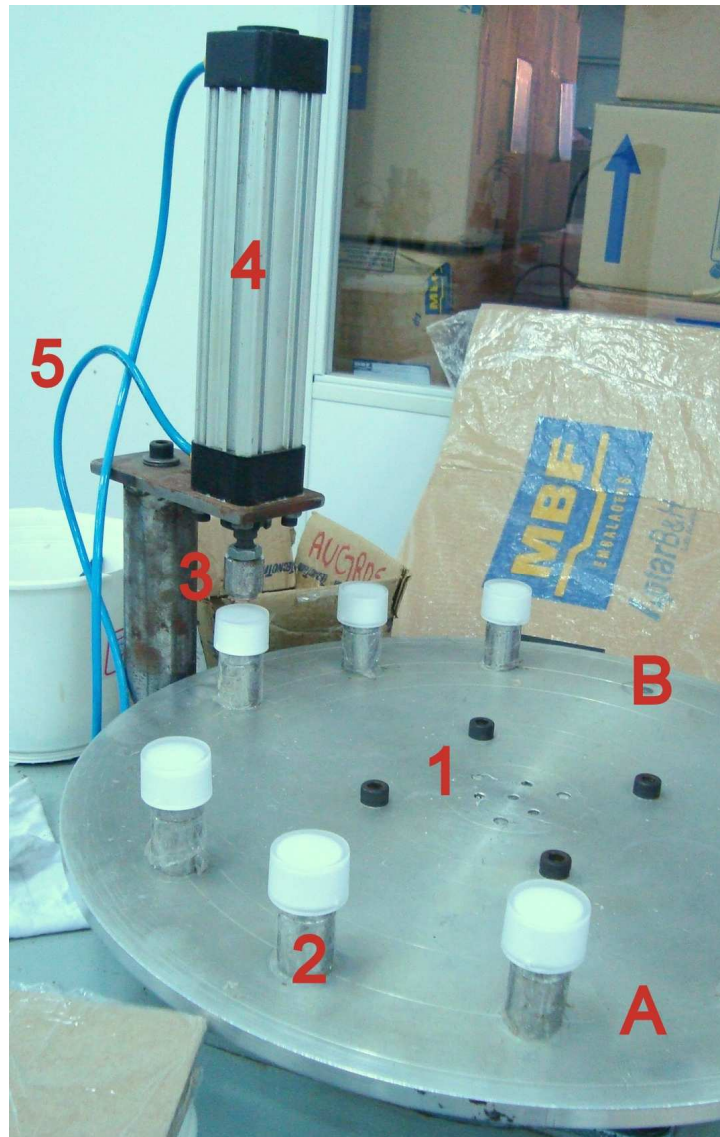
Máquina automática para encaixe de tampas e sobretampas
